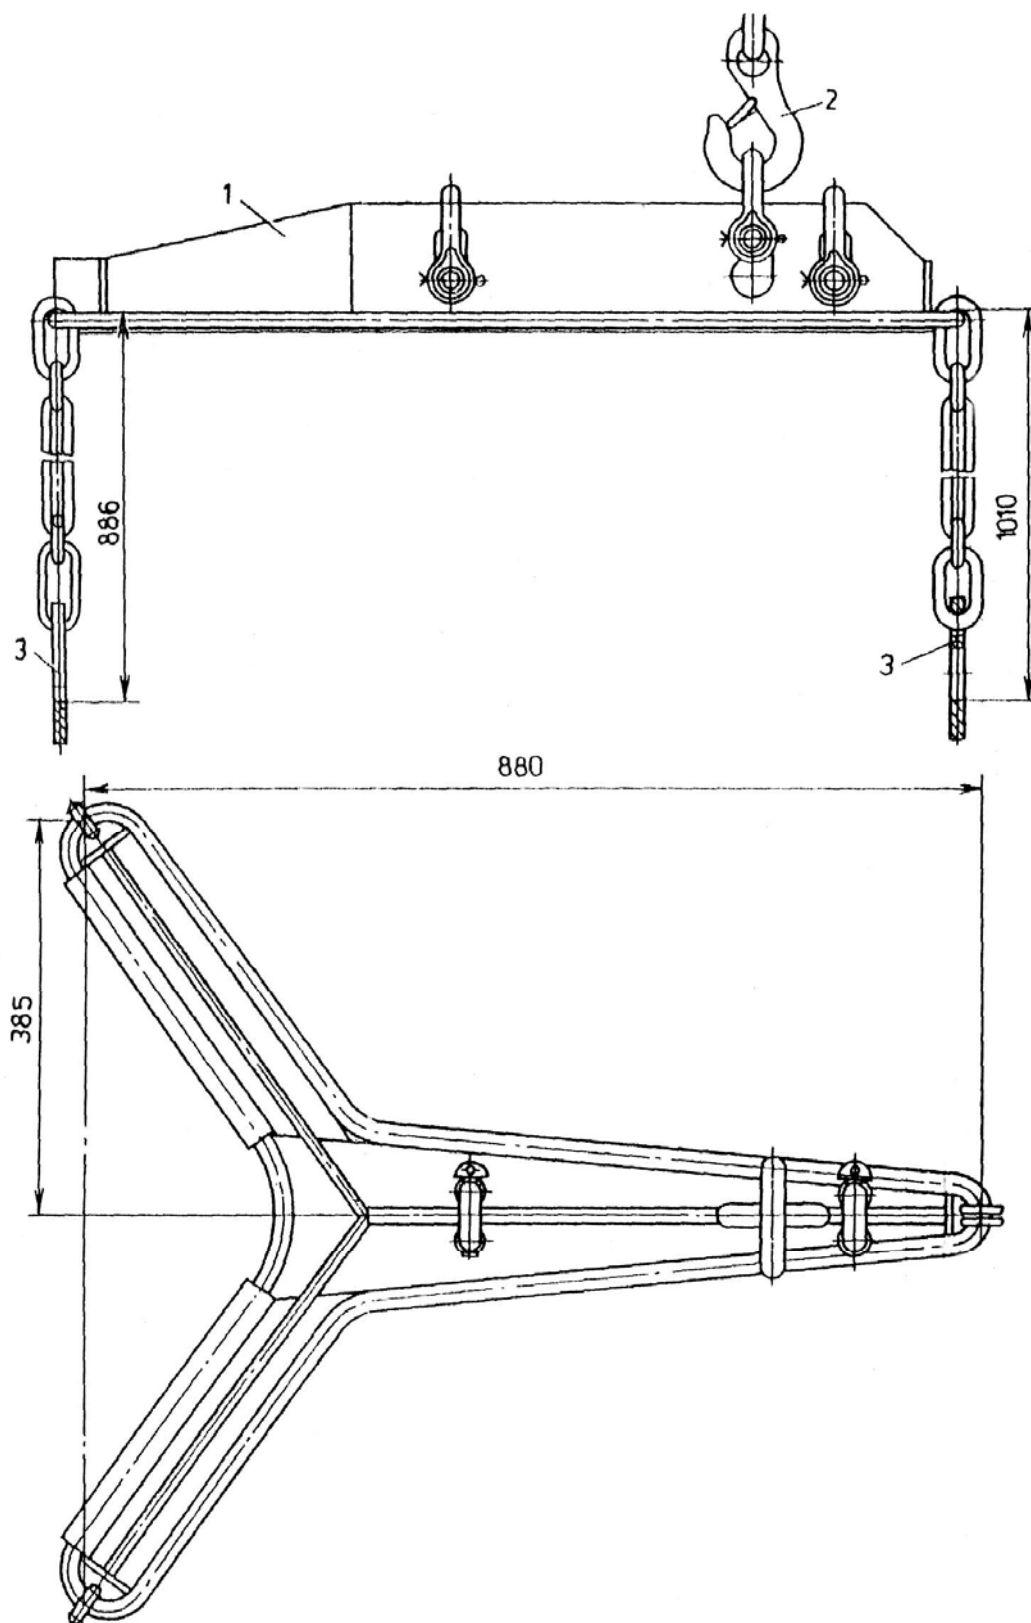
Грузозахватное приспособление для подвеса силового агрегата:
